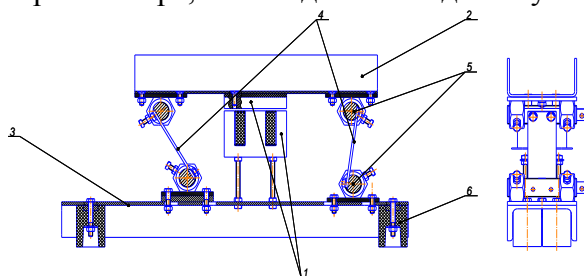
Конструктивна схема вібраційного конвеєра з довільно розташованими плоскими пружинами.
